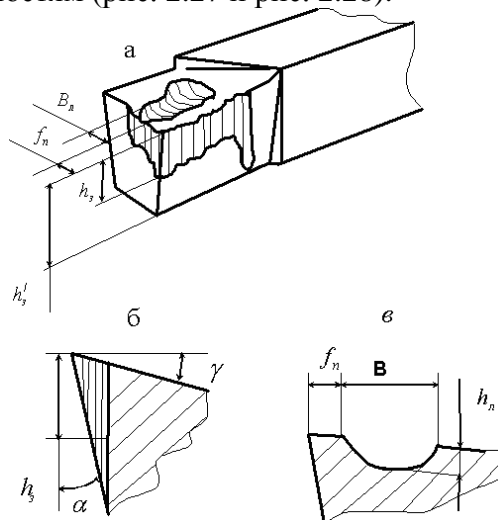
Распределение износа по поверхностям инструмента: а – общий вид режущей части инструмента со следами износа; б – износ по задней поверхности; в – износ по передней поверхности.
